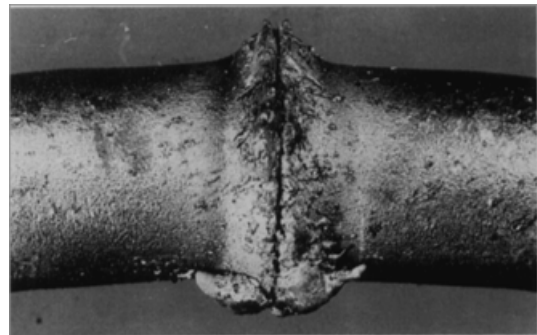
Stauchgrat einer Abbrennstumpfschweißverbindung an einem Kettenglied;
